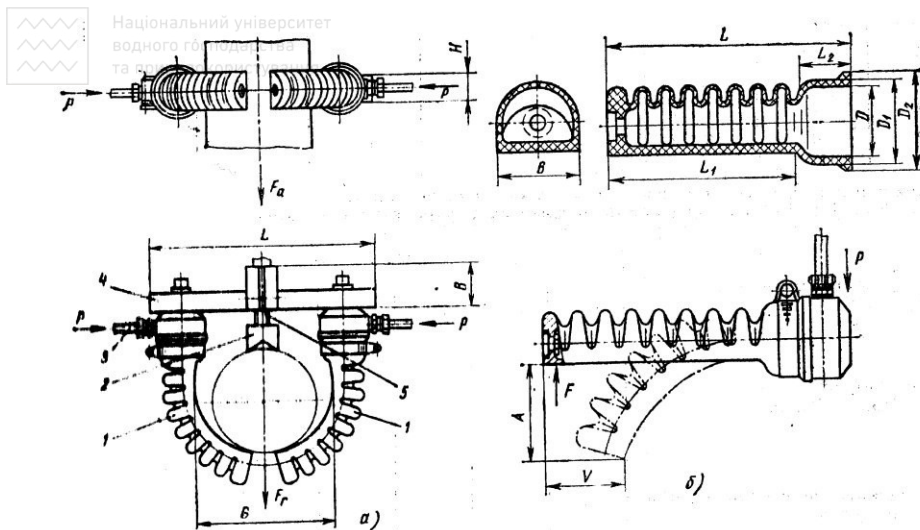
Захватний пристрій із згинаючими еластичними камерами:
